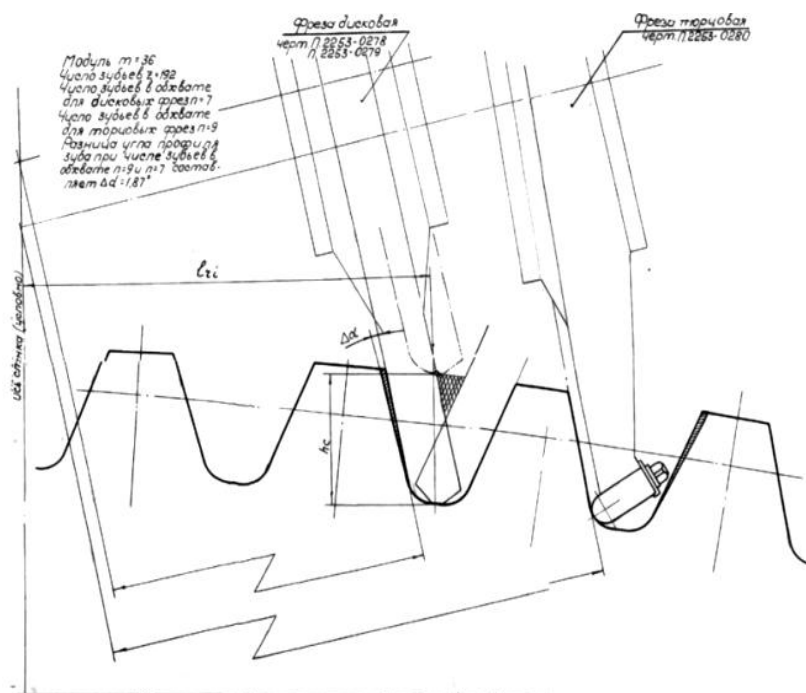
Схема установки дисковых прорезных и торцевых чистовых фрез
